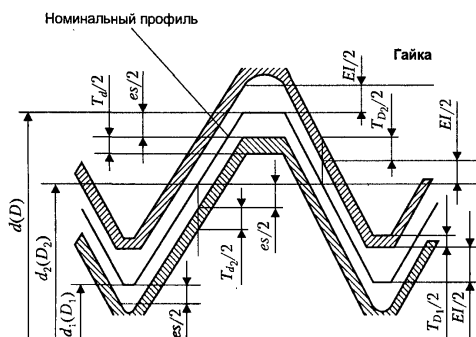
Расположение полей допусков резьбы при посадке с зазором
